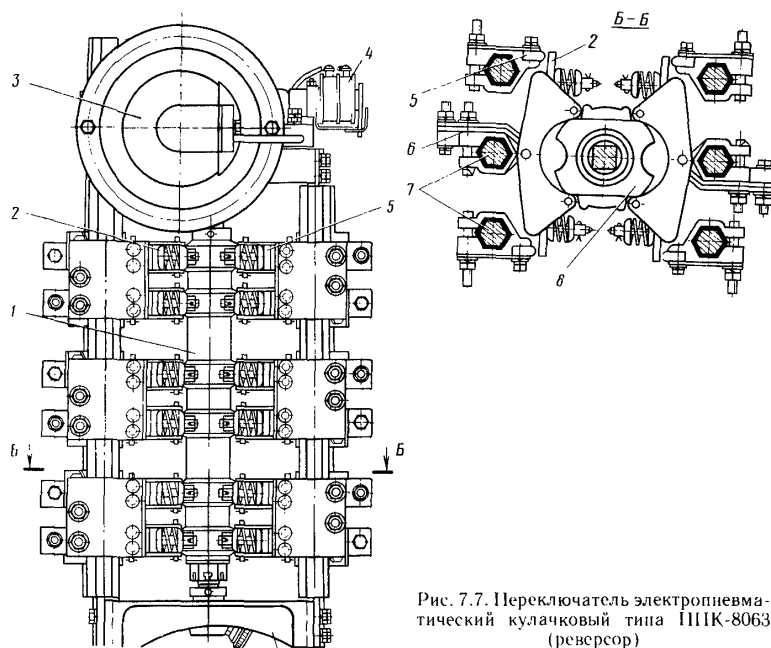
Переключатель электропневматический кулачковый типа ППК-8063 (реверсор)
